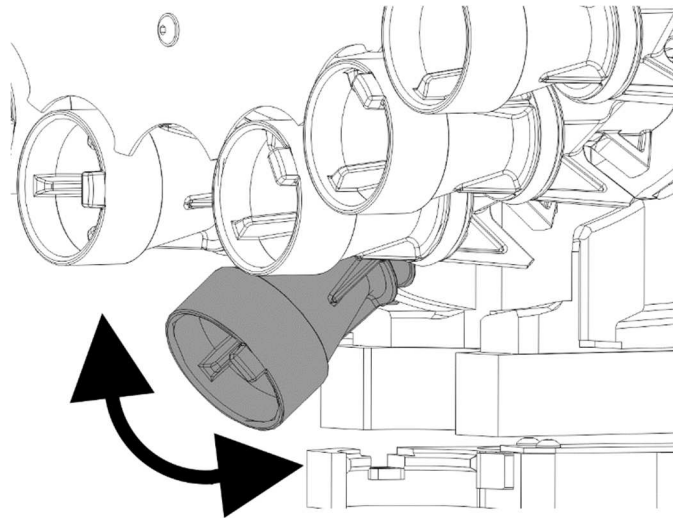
Výměna nástroje pomocí robotického manipulátoru [5]
